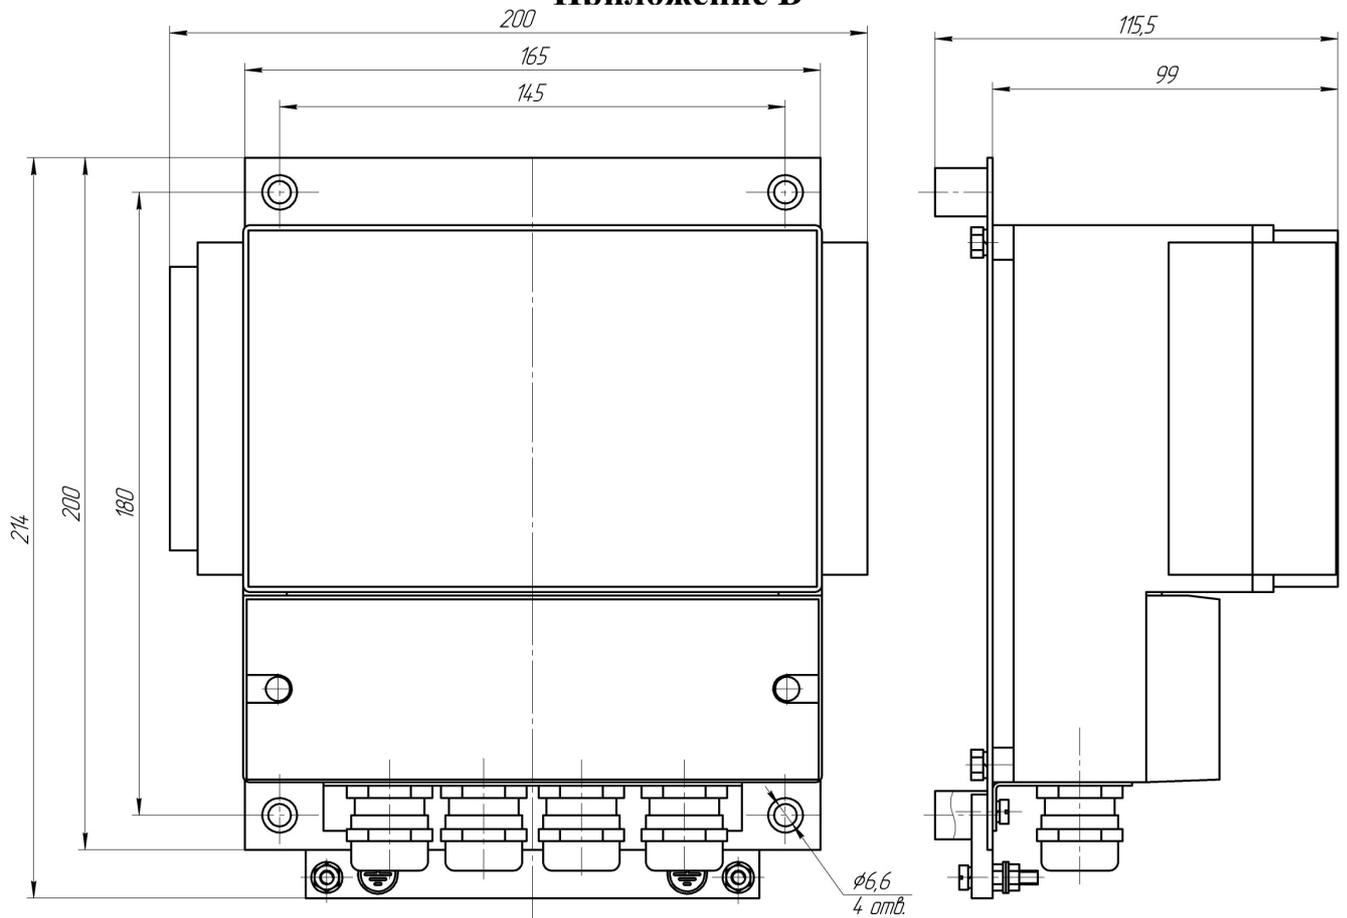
Измерительный прибор рН-метра рН-4122.АС
